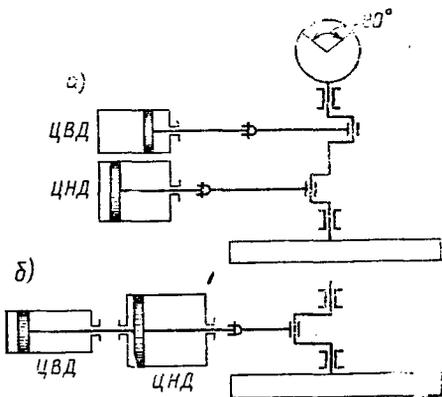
Схема расположения цилиндров и вала машин компаунд (а) и тандем (б)
